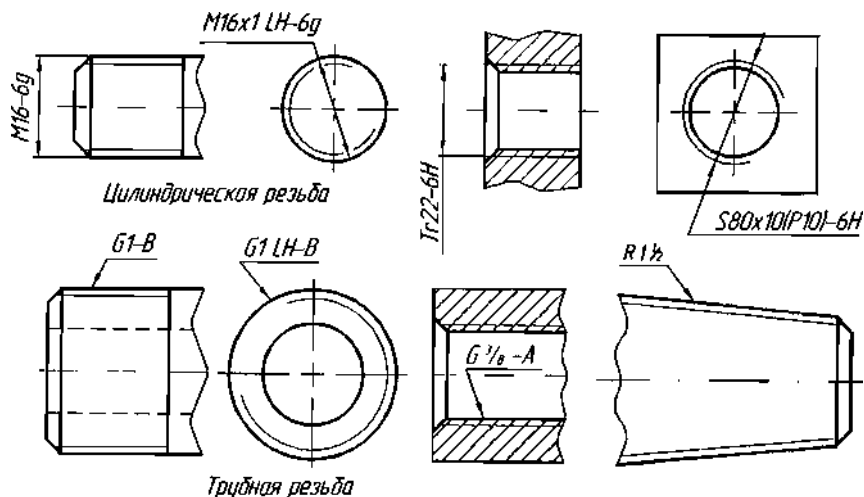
Примеры нанесения обозначений резьб на чертежах
